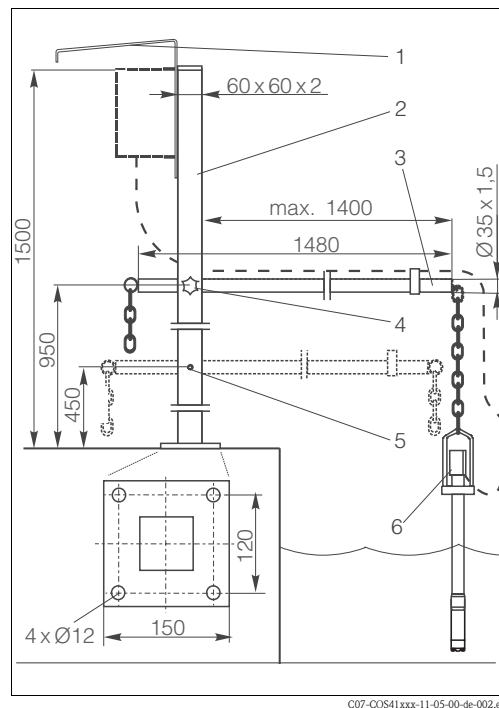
Universalarmaturenhalterung mit Eintauch-Pendelarmatur
